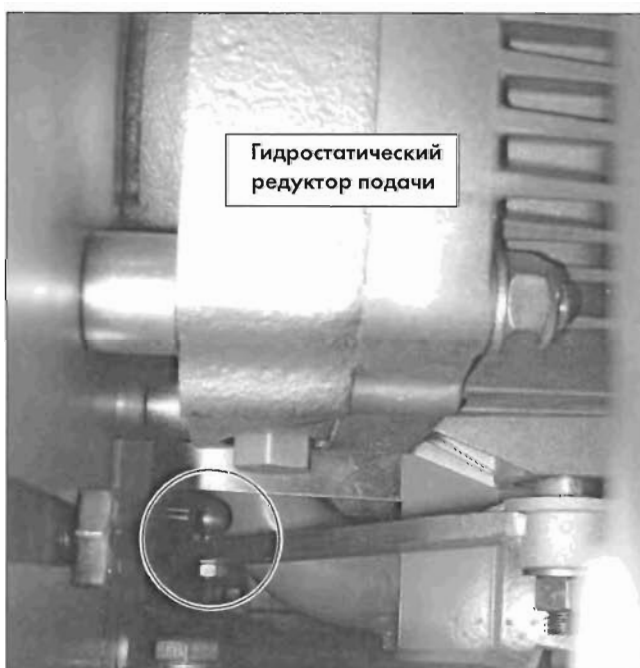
Трос Бодена на корпусе редуктора подачи, в направлении к гидростатич. редуктору
